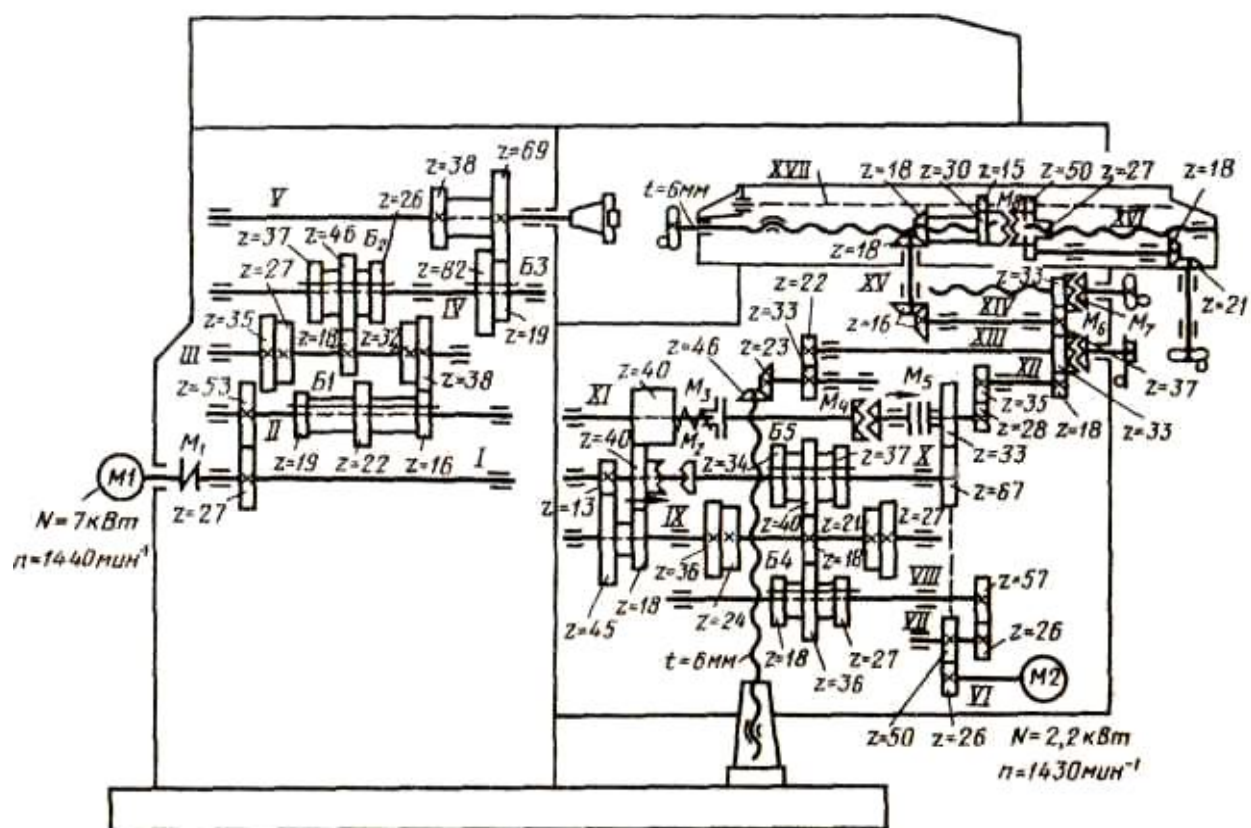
Кинематическая схема станка 6P82Г
